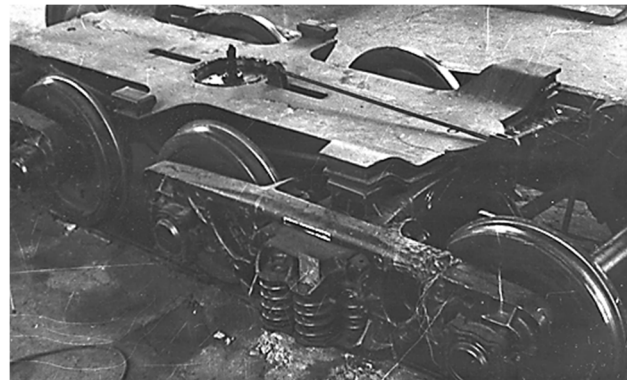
Четырехосная тележка со штампо-сварной соединительной балкой
